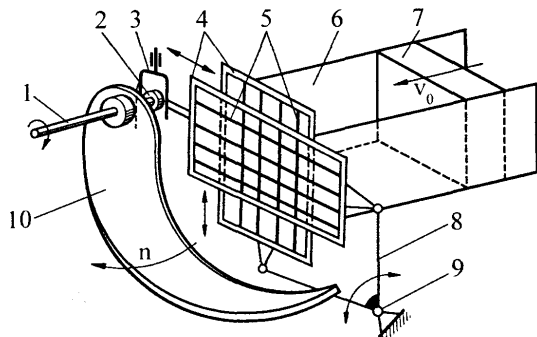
Принципиальная схема режущего узла шпигорезки:
